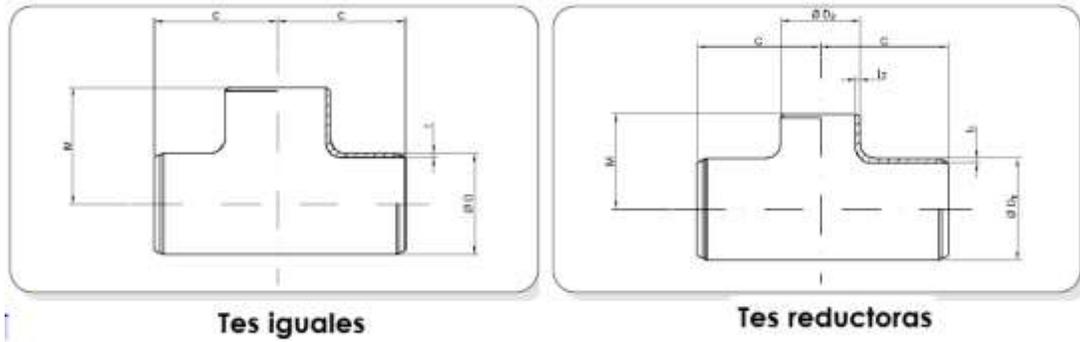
Tipos de TEE. Fuente: Catalogo Tubos y accesorios en acero al carbono soldado y sin soldadura Normas EN (DIN) y ASTM. Tubasol S.A
